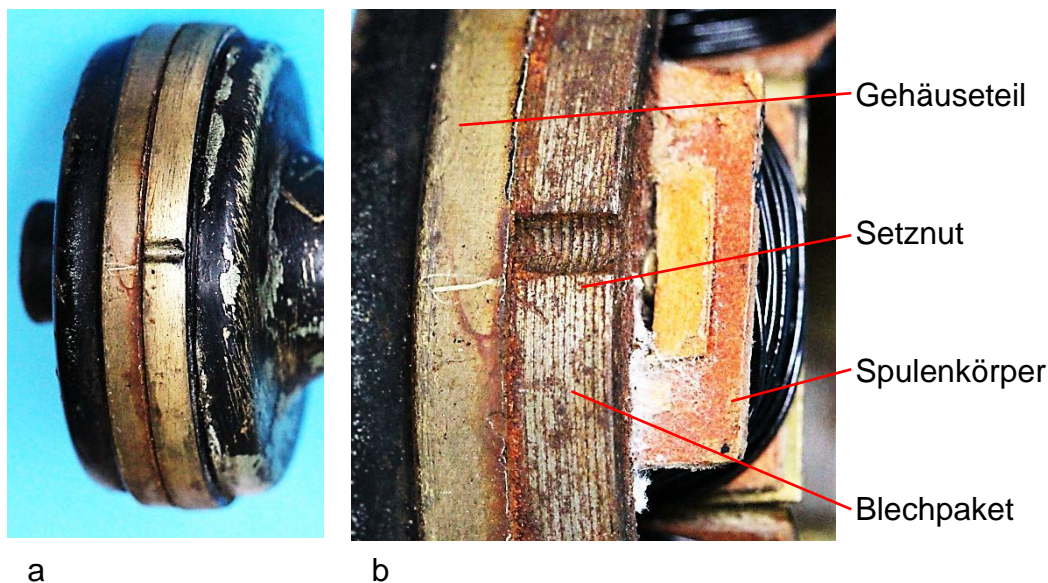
Montage der Gehäuseteile: a) Spalt zwischen den gehäuseteilen, b) Blechpaket kraftschlüssig in einem Gehäuseteil eingesetzt
